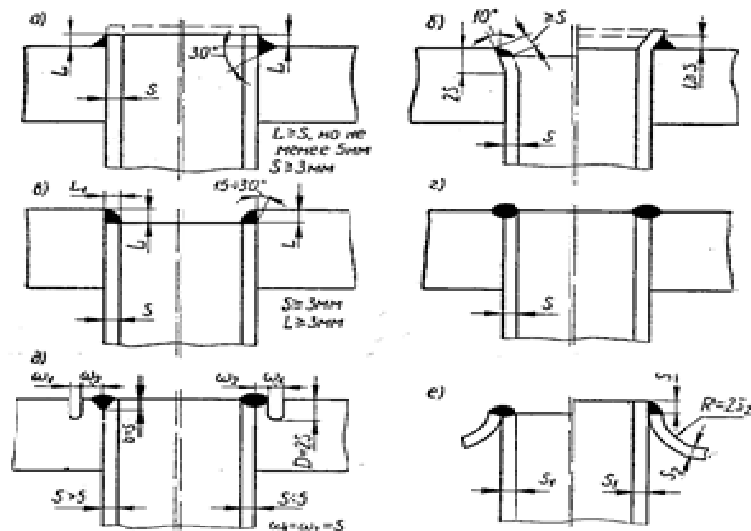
Типи зварних з'єднань труб з трубними дошками:
